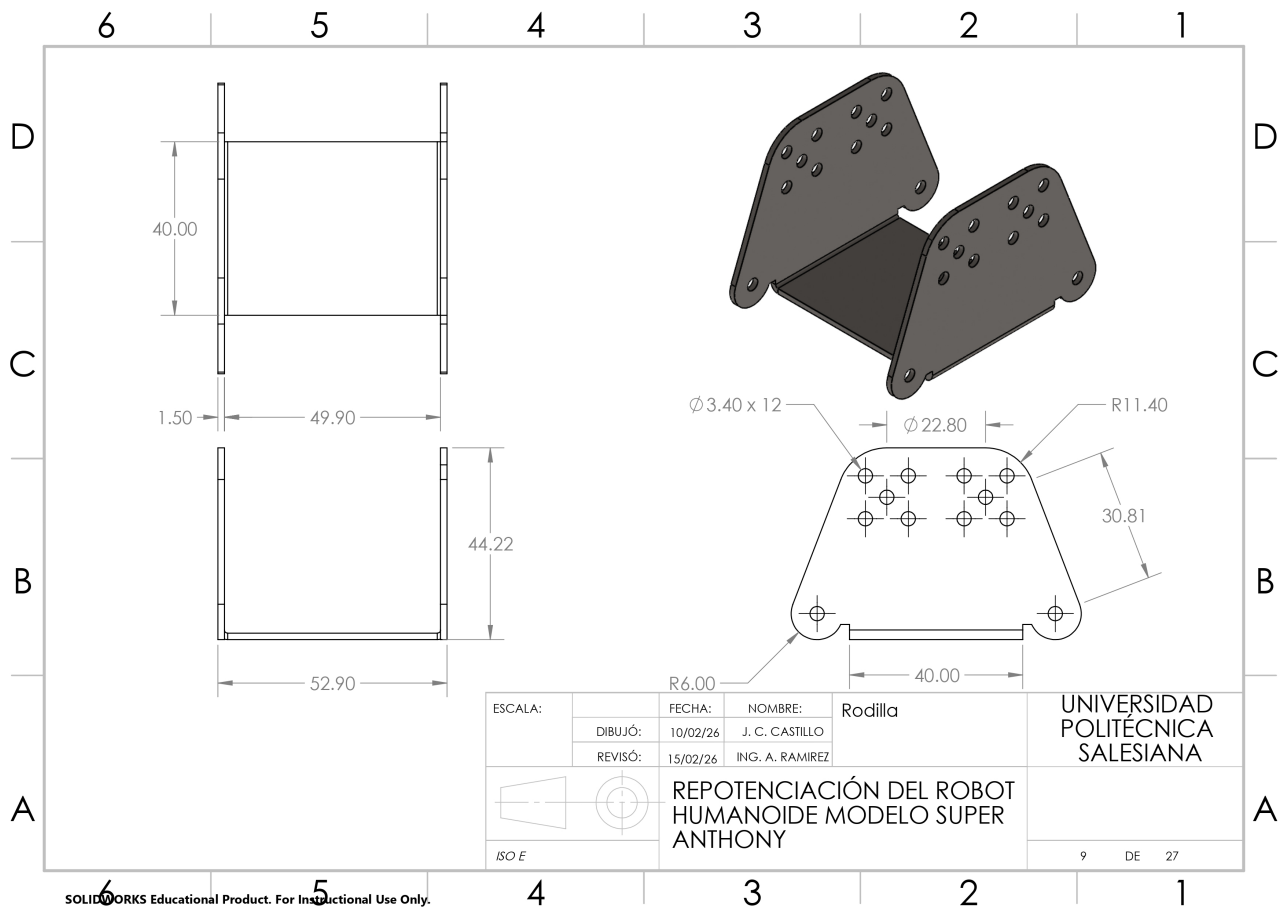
Lámina acotada de la rodilla del robot humanoide, por J. Castillo y B. Gualle, Solidworks
